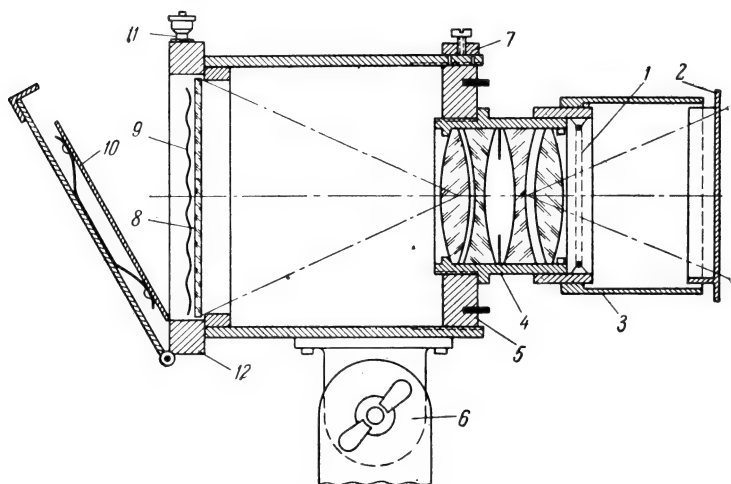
Схема устройства камеры для фотографирования метеоров. 1 — провода подогрева, 2 — крышка, 3 — противоросник, 4 — объектив, 5 — резьба фокусировки; 6 — винт крепления; 7 — стопор, 8 — прижимное стекло, 9 — фотопленка, 10 — прижимная пластинка; 11 — защелка крышки кассеты, 12 — корпус кассеты.
